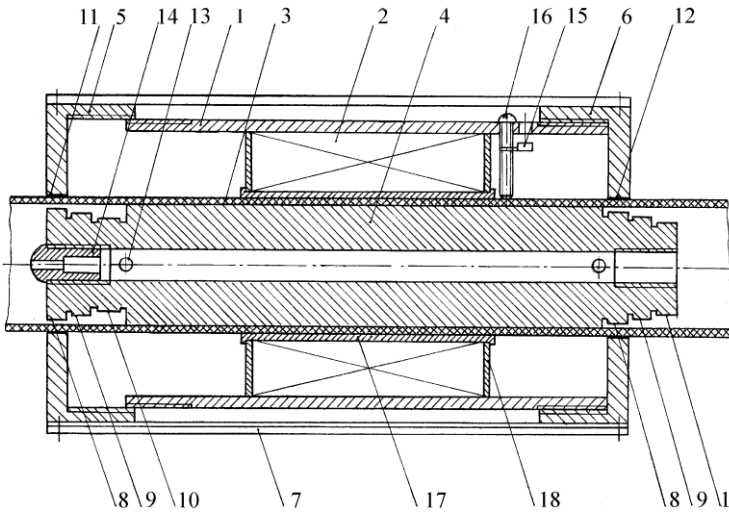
Установка трубчатая водомагнивающая проточная, 1-цилиндрический магнитопровод, 2-намагнивающая катушка, 3- немагнитный трубопровод, 4- полый сердечник, 5, 6- торцевые крышки, 7- тяга, 8, 9, 10- ступени сердечника, 11, 12- поверхности сквозных отверстий торцевых крышек, 13- осевые отверстия, 14- заглушка, 15- штекерный разъем, 16- фиксирующий винт, 17- гильза катушки, 18- шека.
